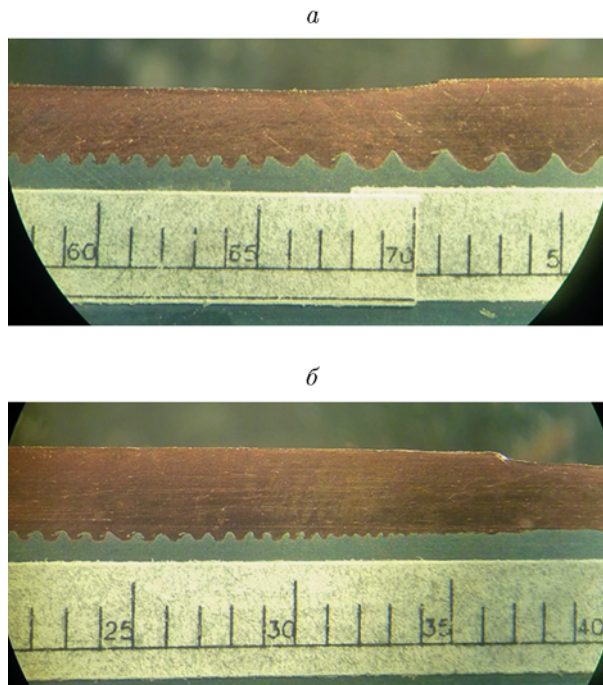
Зона сварки медной и стальной пластин: волны перед выступом и сразу за ним (а), волны перед обратной ступенькой выступа (б) (движение фронта детонации слева направо)
